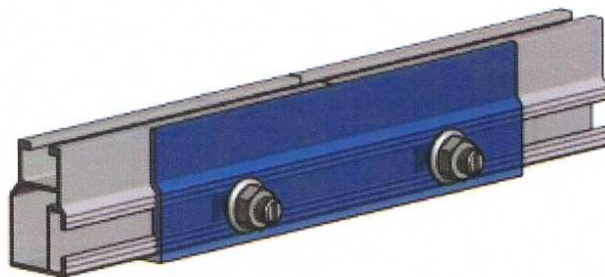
Konstrukcja wsporcza na dachu budynku
